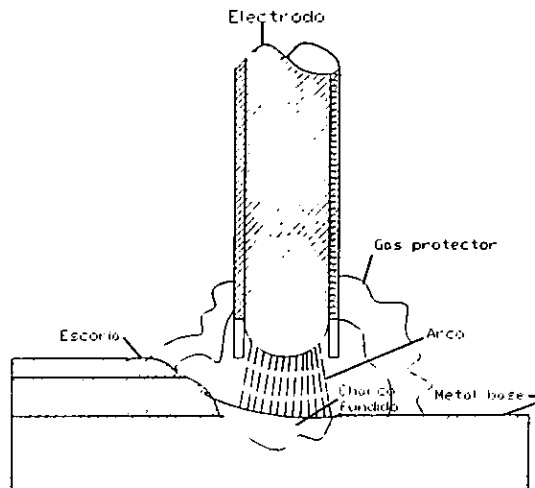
Elementos del proceso de soldadura de arco metálico protegido (SAP)
